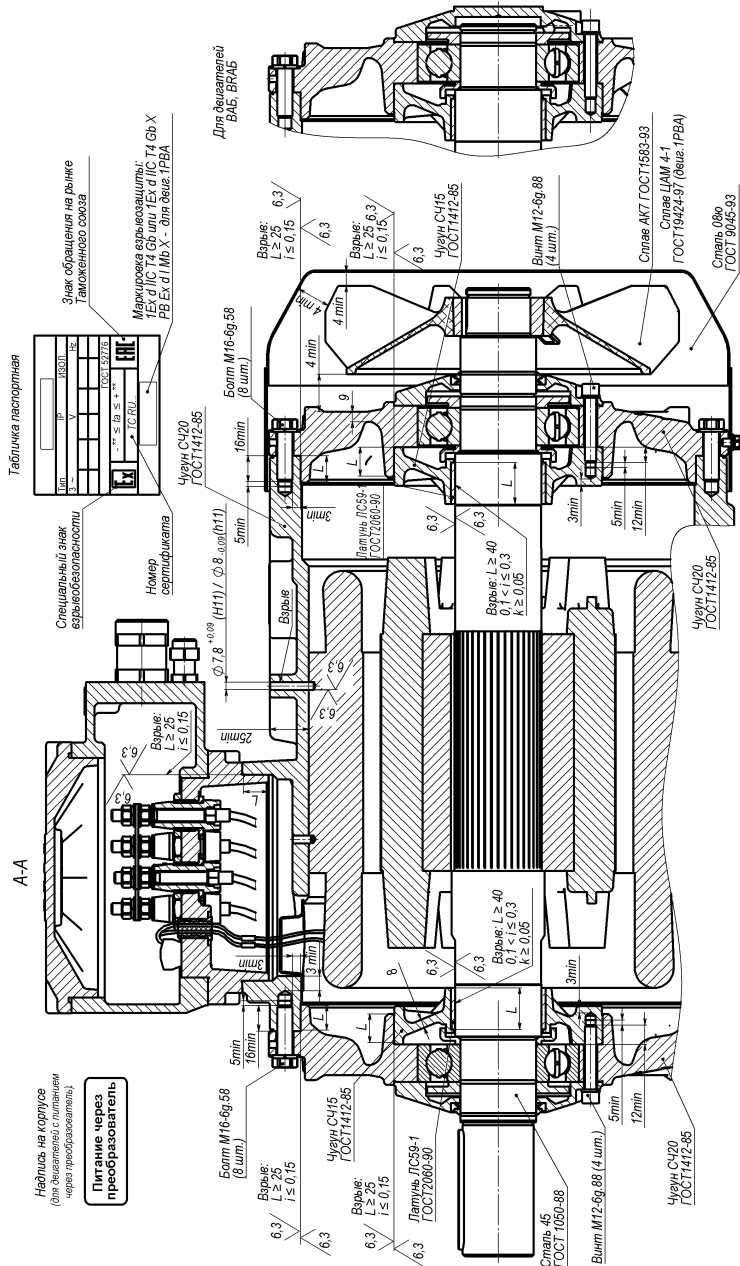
Чертеж взрывозащиты двигателей ВА(Б), IPBA250,280; ВРА(Б), IPBA280,315
